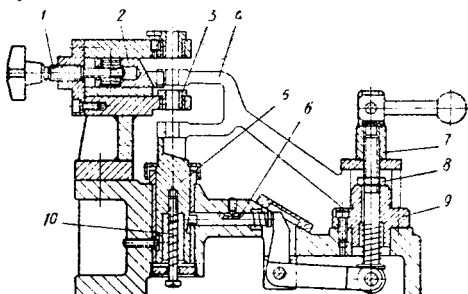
Приспособление для обработки отверстий в изогнутых рычагах
